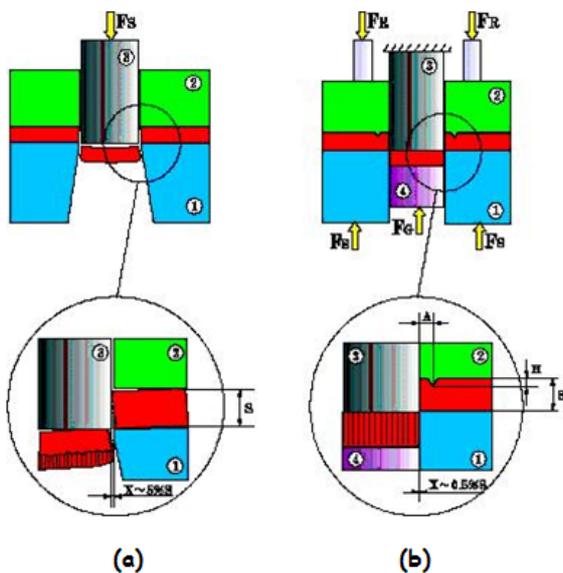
Variantes de corte: a) recorte tradicional (*blanking*) e b) recorte fino (*fine blanking*)
